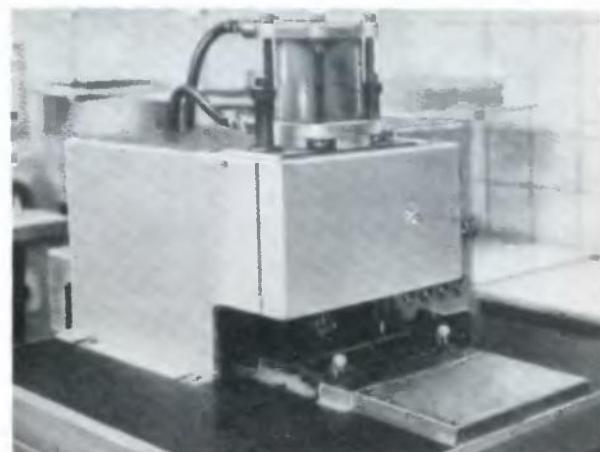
Полуавтомат для безразборного соединения корпуса магнитофона и решетки
